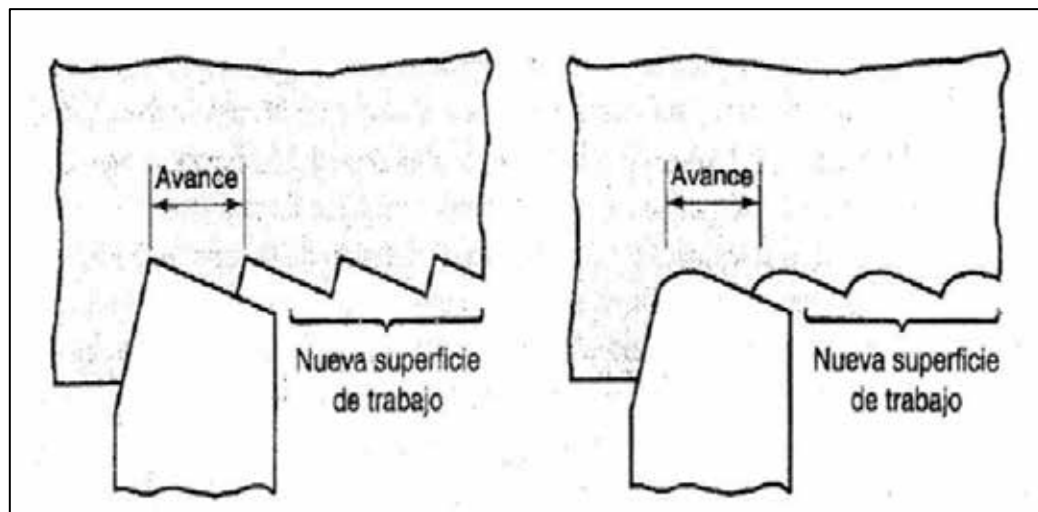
Rugosidad generada por (izquierda) Herramienta de corte con filo y (derecha) Herramienta con radio.
